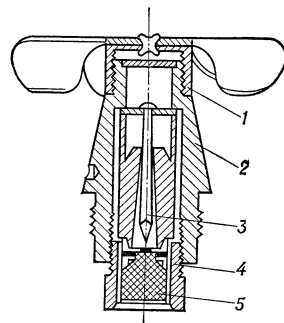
Взрыватель к авиабомбе (механич. ударного действия, головной): 1 — предохранительный колпачок с ветрянкой; 2 — корпус; 3 — ударник; 4 — втулка; 5 — капсуль-детонатор.
